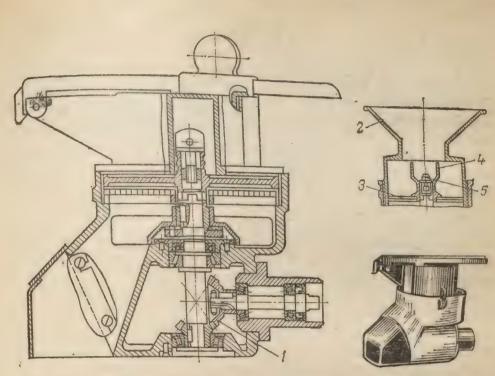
Механизм МОП-II-1 с протирочным приспособлением
